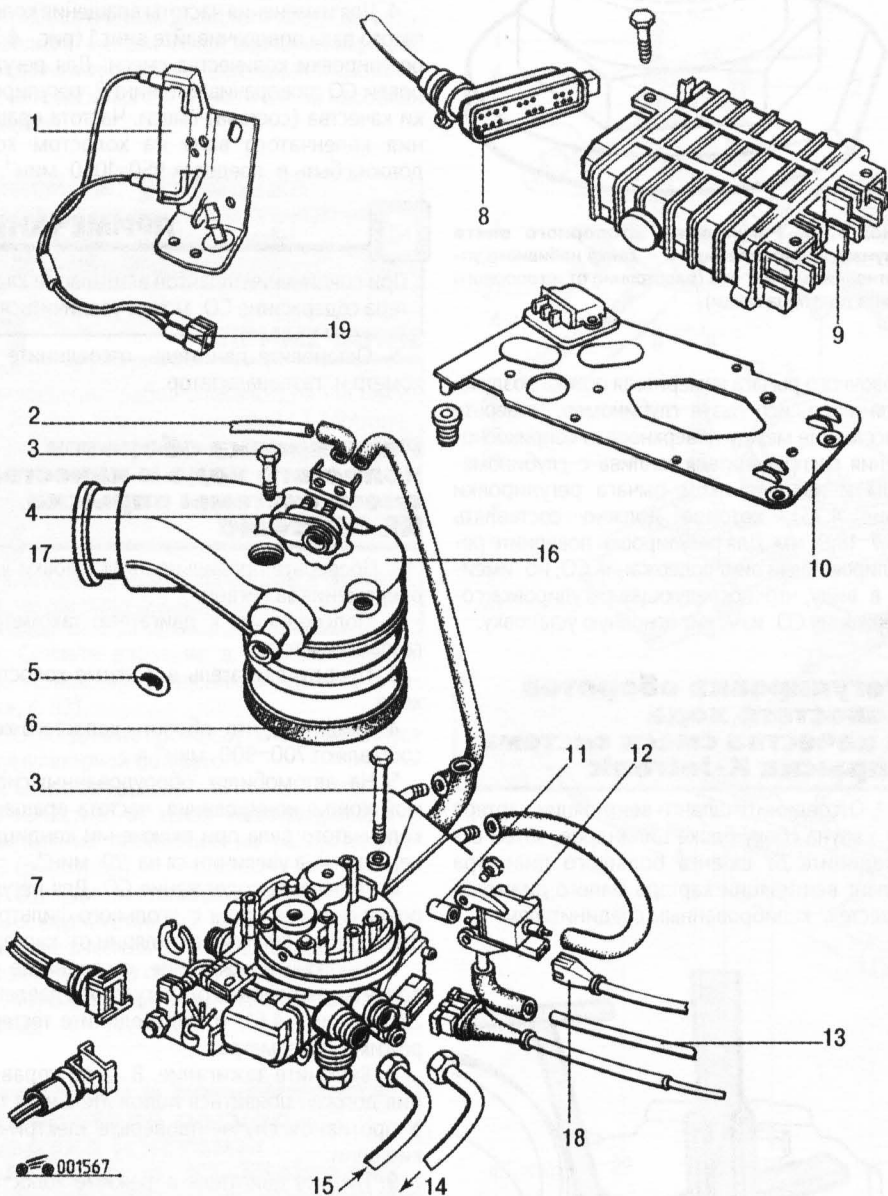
Элементы системы впрыска топлива K-Jetronic: 1 - дополнительный резистор; 2, 13 - вакуумные шланги; 3 - болт; 4 - регулятор температуры поступающего в двигатель воздуха; 5 - крышка клапана; 6 - уплотнительное кольцо; 7 - инжектор; 8 - колодка жгута проводов; 9 - блок управления; 10 - пластина крепления; 11 - вентиляционная трубка; 12 - клапан управления; 14 - трубка возврата топлива (синего цвета); 15 - трубка подачи топлива (черного цвета); 16 - крышка воздухозаборника инжектора; 17 - штуцер воздухозаборника; 18 - колодка жгута проводов; 19 - колодка жгута проводов дополнительного резистора
